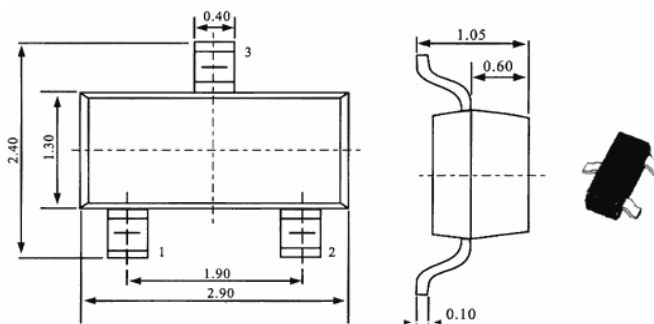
Габаритні розміри корпусу напівпровідникових елементів типу SOT-23
